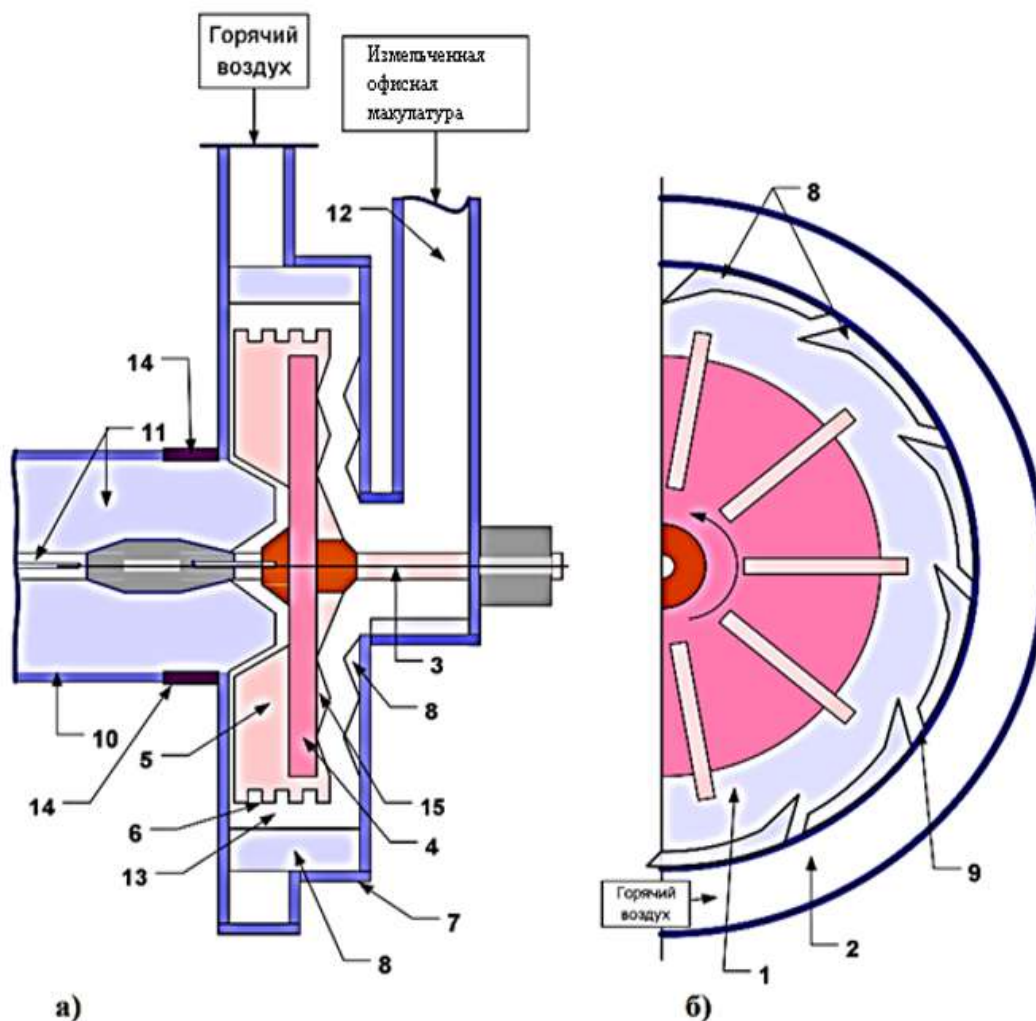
Схема диспергатора (а – вид сбоку, б – вид сверху): 1 – ротор; 2 – улитка для подачи воздуха; 3 – вал; 4 – диск; 5 – лопатки ротора; 6 – ножи; 7 – корпус диспергатора; 8 – статорные элементы; 9 – каналы для подачи воздуха; 10,12 – патрубки; 11,15 – лопатки; 13 – зона активного механического воздействия; 14 – теплоизоляционные вставки [117]
